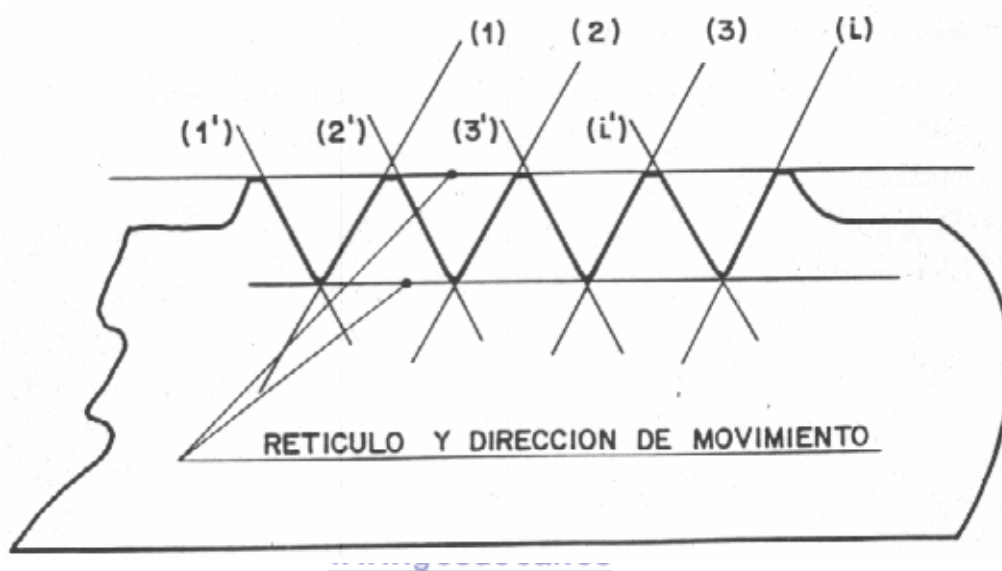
Medidas sobre la imagen proyectada de la plantilla.
